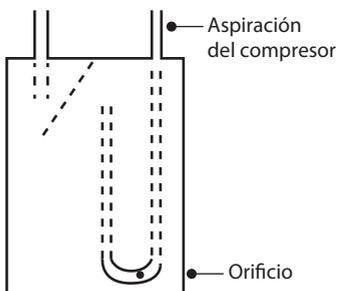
Detalle de seccionado de un acumulador de aspiración.
